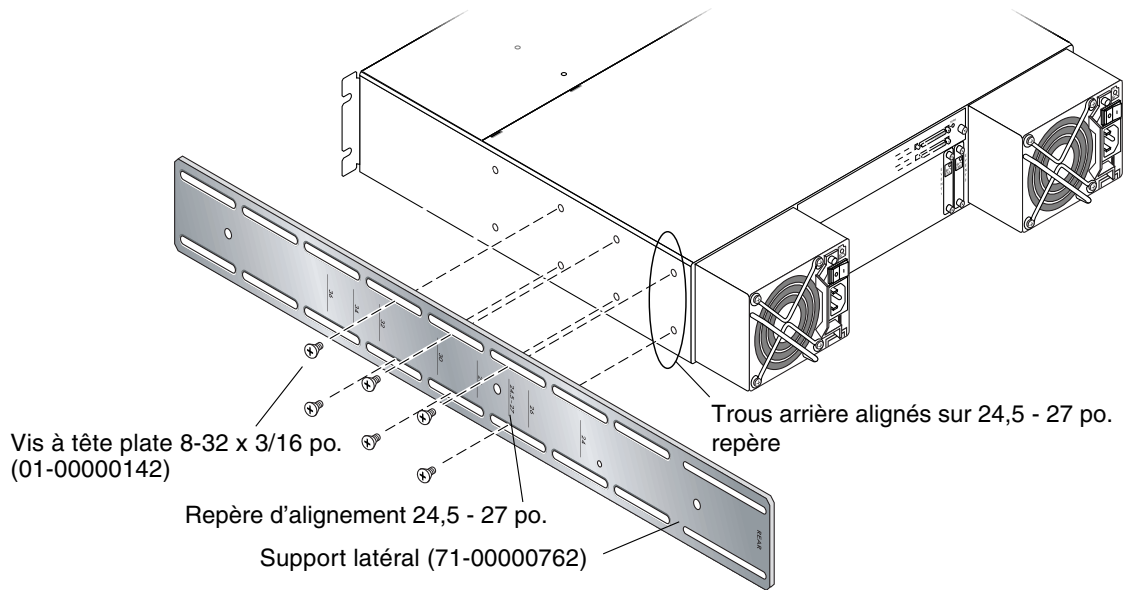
Aligement d'un support latéral sur les trous taraudés arrière du panneau latéral de la baie
